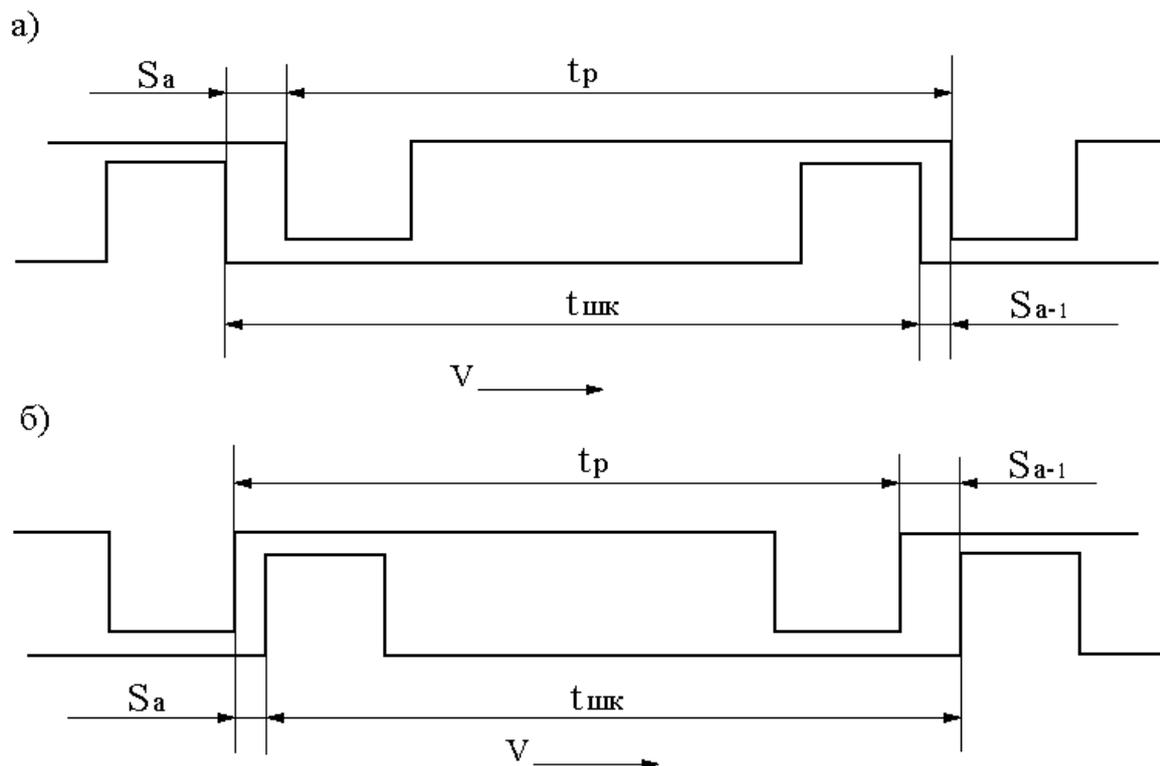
Схема взаимного расположения зубьев: а) ремня и ведущего шкива; б) ремня и ведомого шкива
